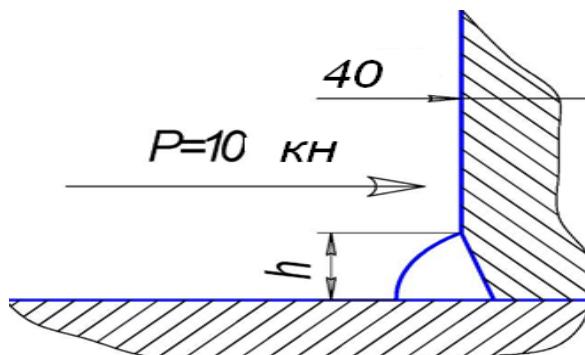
Расчетная схема сварного шва.
